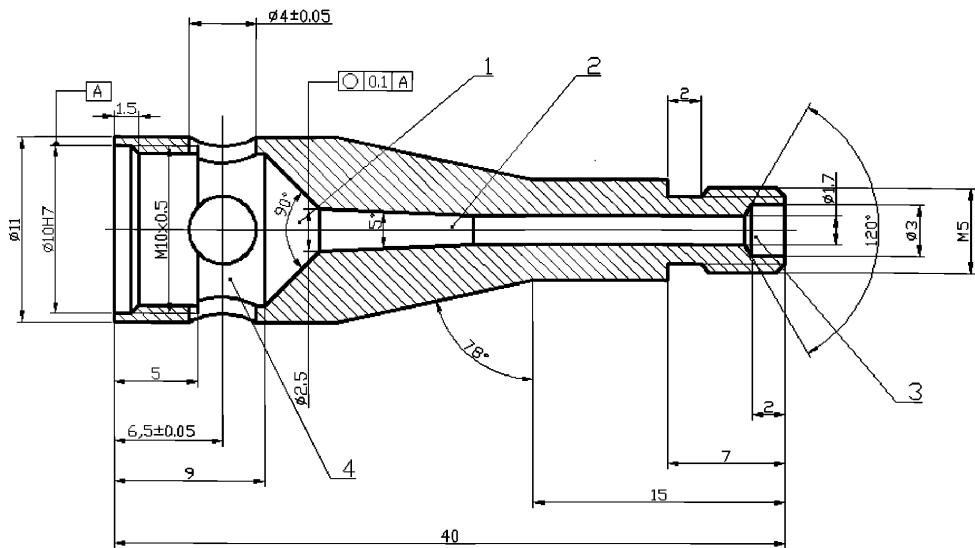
Горелка для зажигания образца (трубка газовой горелки»).
